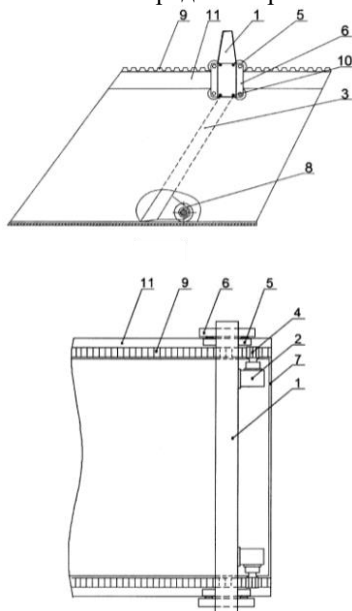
Вид сбоку и сверху: 1 – рама; 2 – планетарный гидромотор-редуктор; 3 – задняя стенка; 4 – шестерни; 5 – колеса; 6 – ходовая тележка; 7 – боковые стенки ковша; 8 – ролики; 9 – зубчатая рейка; 10 – болты; 11 – боковые балки ковша
